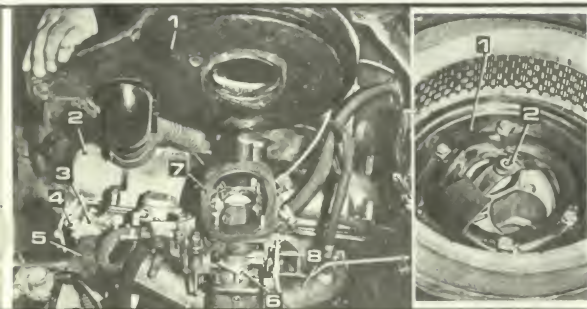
Так выглядит верхняя часть двигателя «Москвич-412» с новым карбюратором и термостатом и старым корпусом воздушного фильтра: 1 — корпус воздушного фильтра; 2 — верхняя крышка двигателя; 3 — фланцевый патрубок отбора жидкости из головки блока; 4 — датчик температуры охлаждающей жидкости; 5 — датчик на нижнем шкиве которого закреплён термостат; 6 — карбюратор; 7 — резиновая прокладка; 8 — впускной коллектор.
